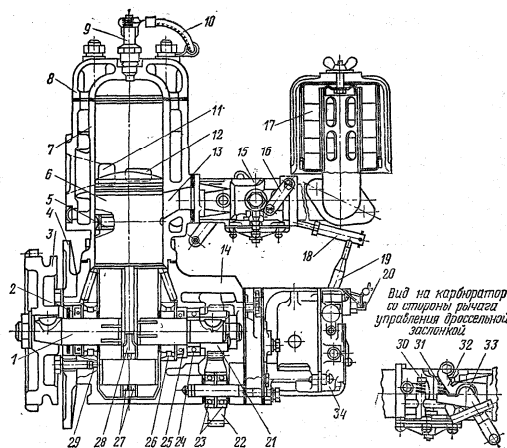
Пусковий двигун: 1 – колінчастий вал; 2 і 25 – манжети; 3 – маховик; 4 – плита; 5 – поршневий палець; 6 – поршень; 7 – циліндр; 8 – головка циліндра; 9 – свічка; 10 – провід; 11 – випускне вікно; 12 – регулятор; 13 – проміжоточна шестерня; 14 – картер; 15 – карбюратор; 16, 19, 32, 33 – важелі; 17 – очисник повітря; 18 – тяга; 20 – регулювальний болт; 21 і 22 – шестерні; 23, 24, 25, 26 і 29 – підшипники; 27 – ролик; 28 – шатун; 30 і 31 – гвинти; 34 – корпус
